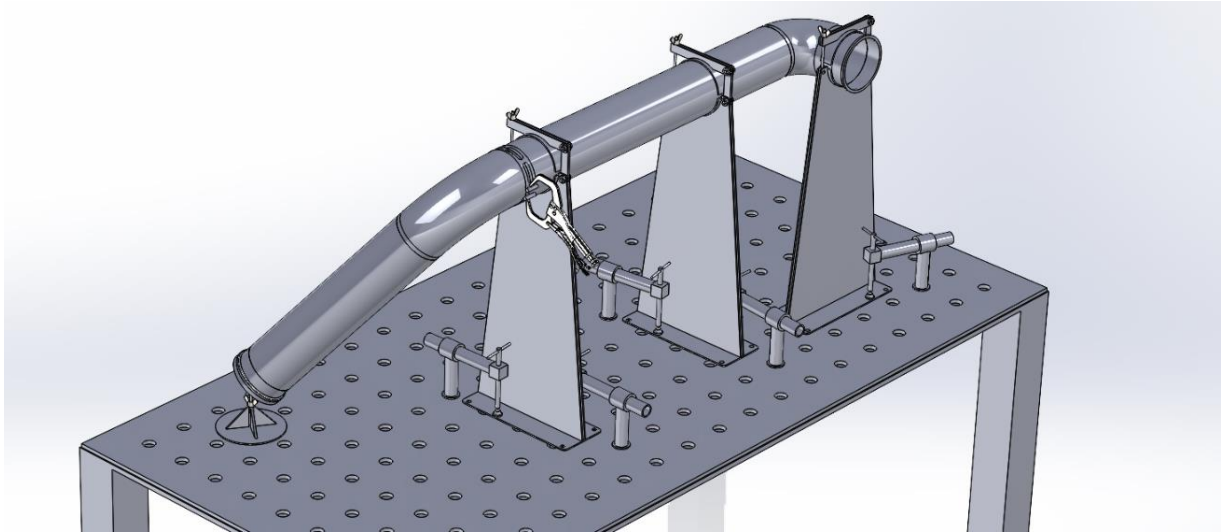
Розташування заготовок при зварюванні шва № 5
